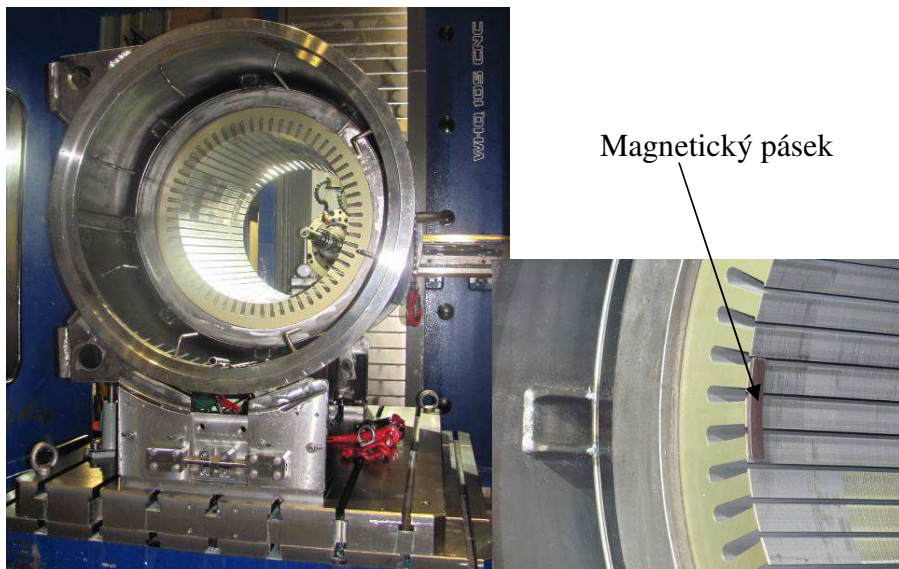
Usazení statoru v přípravku s prizmatickým uložením
